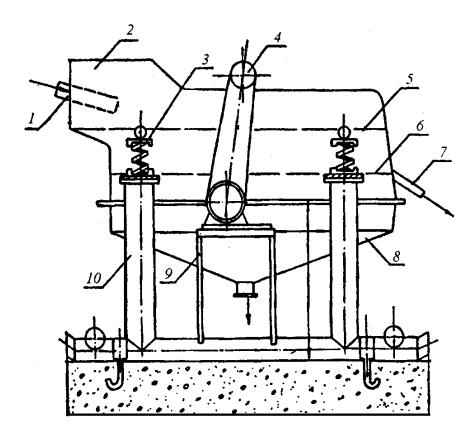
Схема установки виброфильтра: 1 - распределительный лоток; 2 - короб; 3 - амортизатор; 4 - вибратор; 5 - сито верхнее; 6 - сито нижнее; 7 - лоток отвода твердой фракции; 8 - поддон; 9 - электродвигатель; 10 - поддерживающая рама
